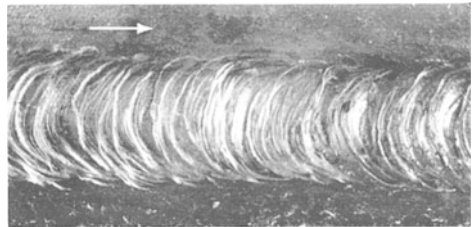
Kehlnaht an 10 mm-T-Stoß (Nachrechtsschweißung).
